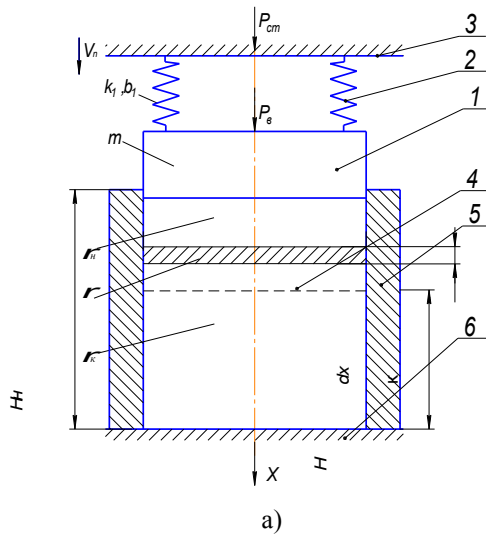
Расчетная схема процесса деформирования порошковой заготовки:
